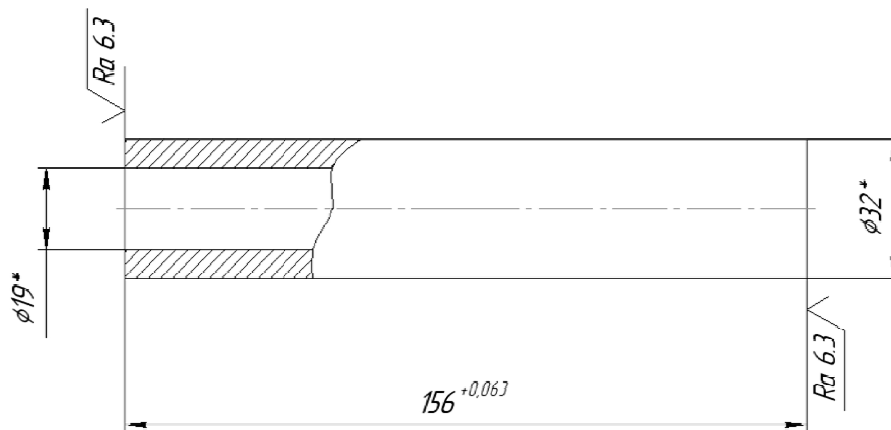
Ескіз заготовки для деталі «Перехідник»
